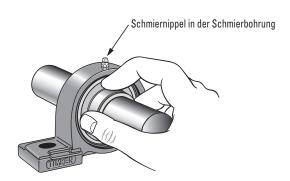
Installation des Schmiernippels im Gewindeschmierloch.
